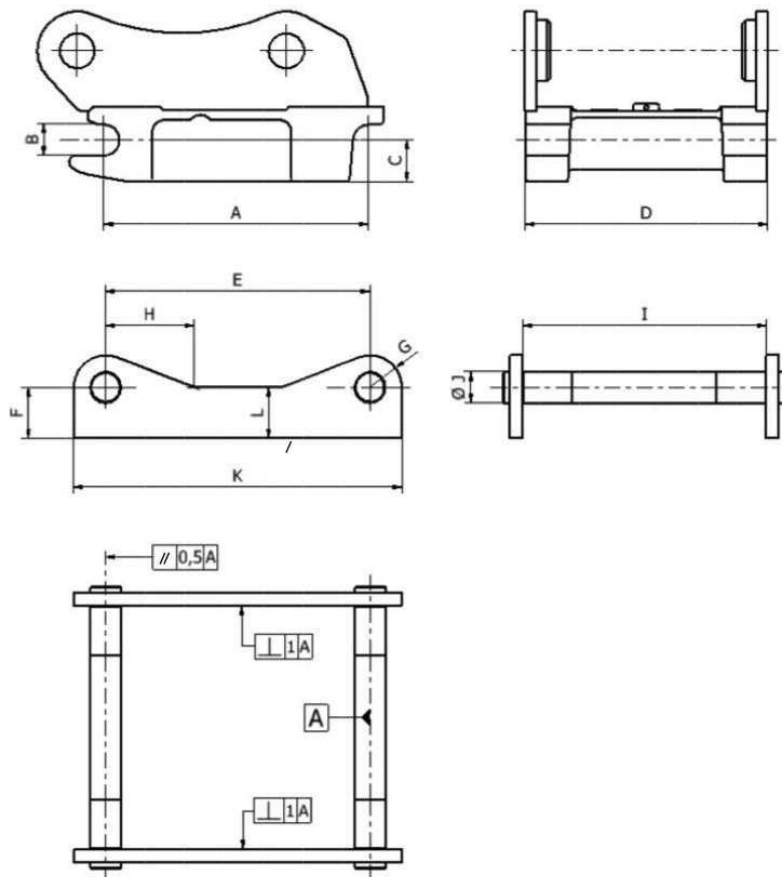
Eliminace tolerancí v zadním upínacím čepu
